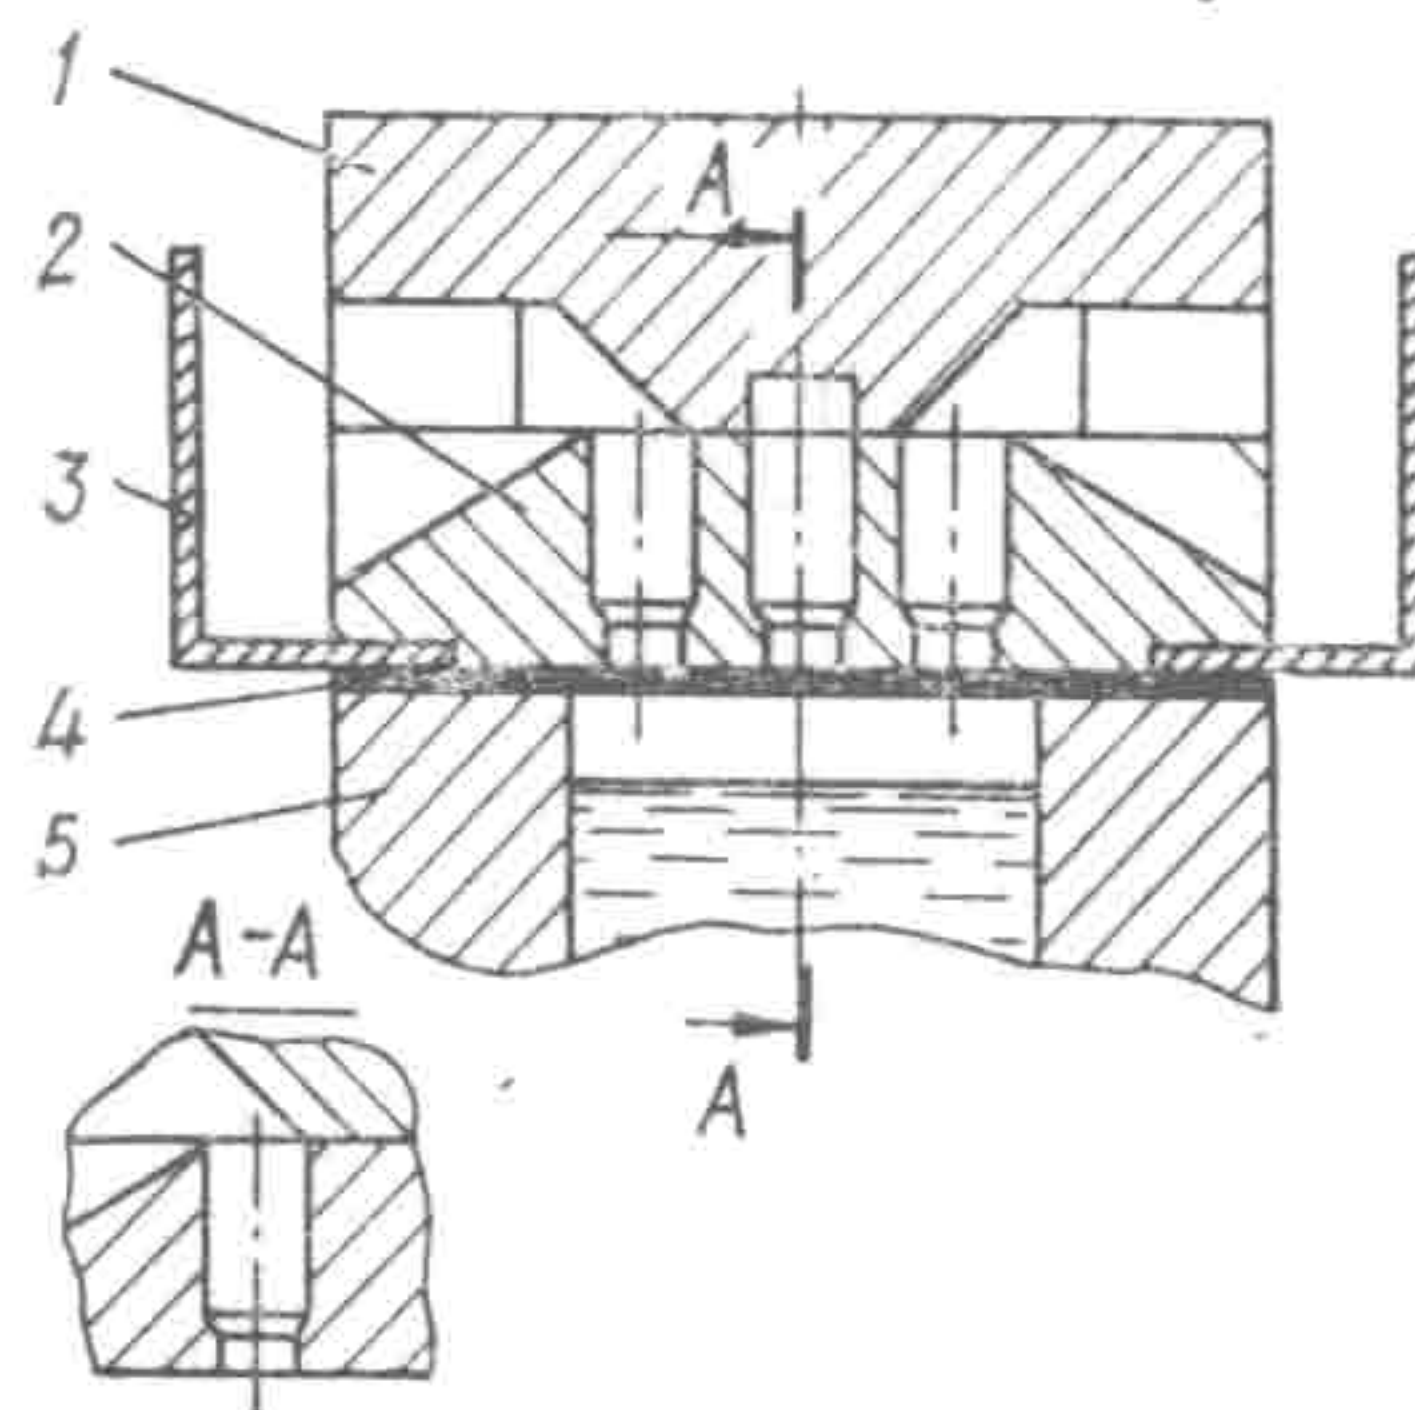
Схема оснастки для пробивки с нижним расположением разрядной камеры:
